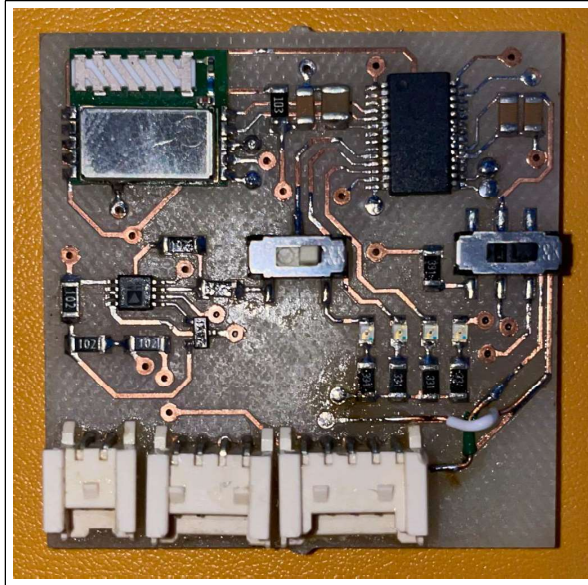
Placa soldada del prototipo final con PIC18F27J13
